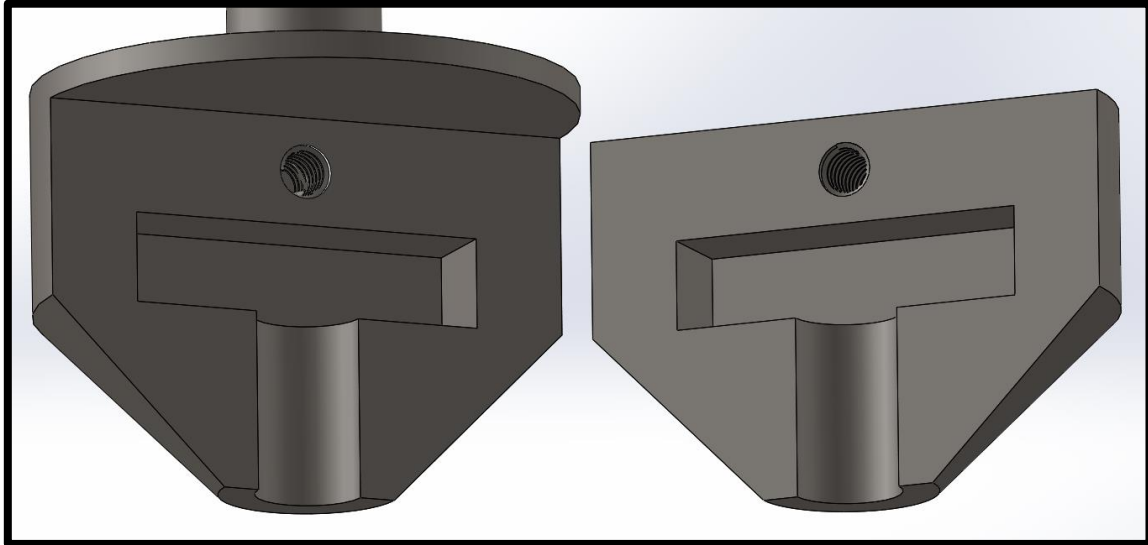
Mordaza hembra (izquierda) y macho (derecha). Fuente: Propia.
